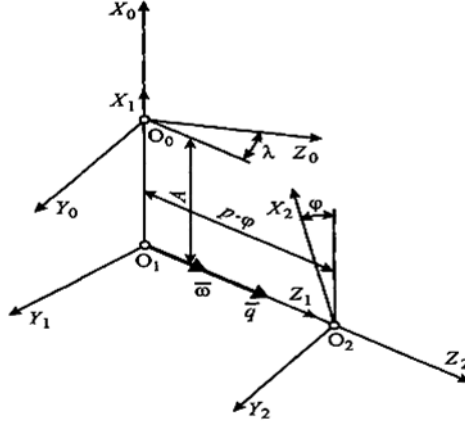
Координатна схема формоутворення ведучого круга для оброблення конічних поверхонь
